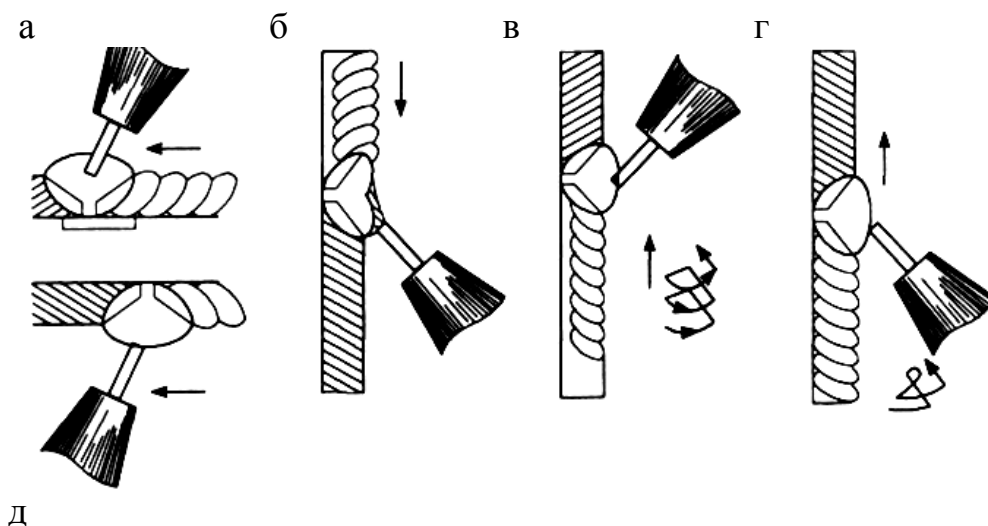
Схемы расположения шва и поперечные колебания электрода при полуавтоматической сварке в углекислом газе
